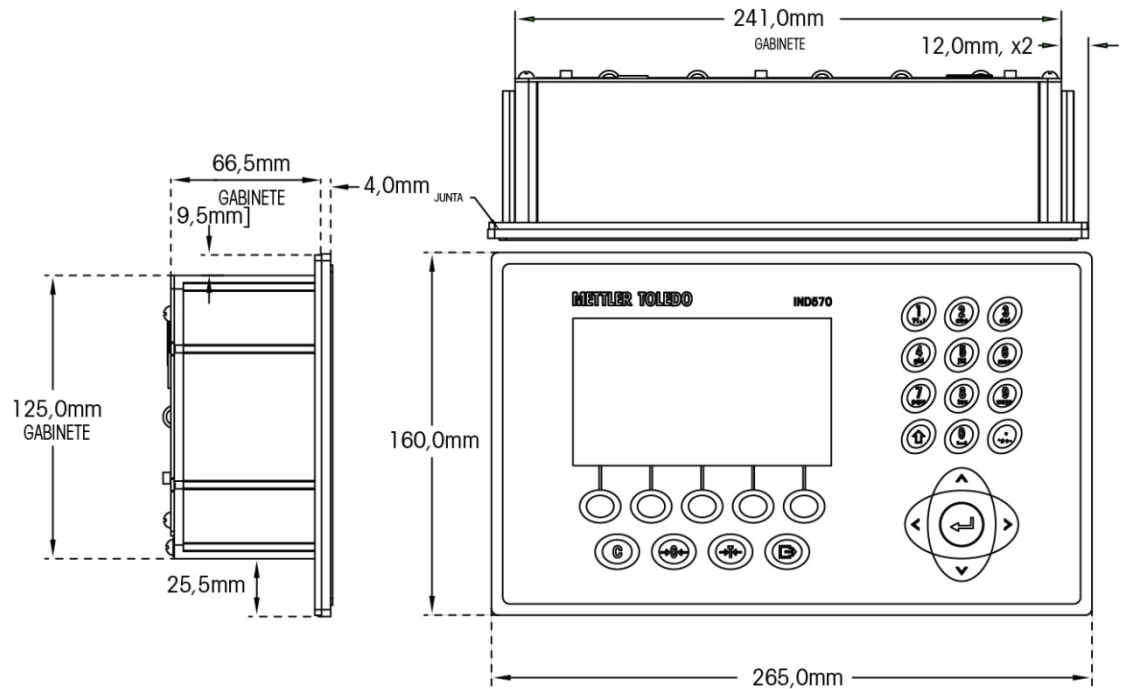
Dimensões do Gabinete do IND570 para Montagem em Painel
